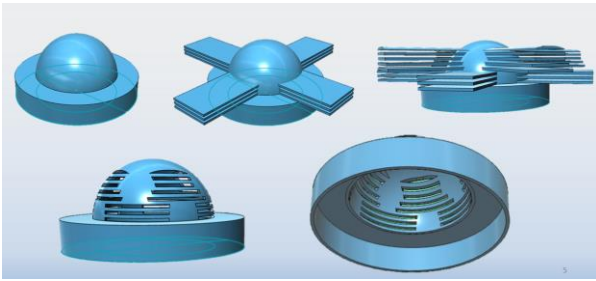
Этапы разработки верхней части корпуса датчика дыма
